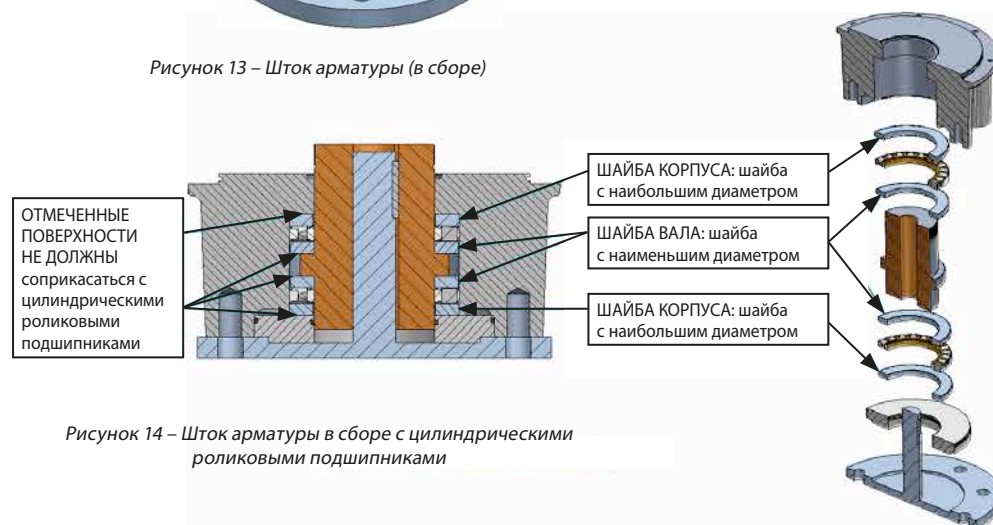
Шток арматуры в сборе с цилиндрическими роликовыми подшипниками
